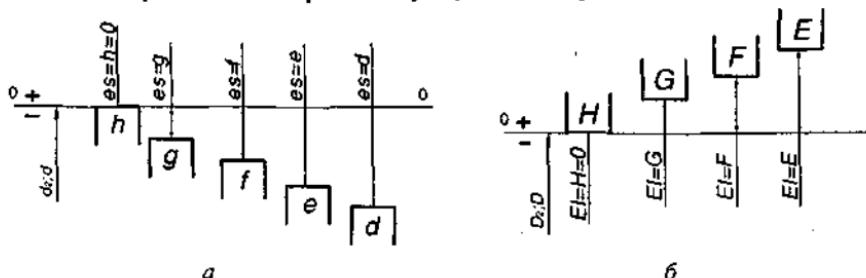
Основные отклонения: а – для болта; б – для гайки
